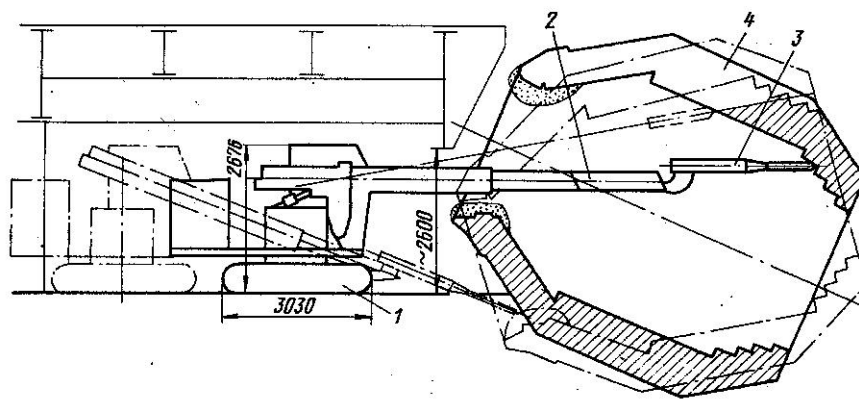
Ломка футеровки конвертера с отъемным днищем: 1 — ходовая часть машины для ломки футеровки; 2 — удлинитель; 3 — пневмомолот; 4 — конвертер
